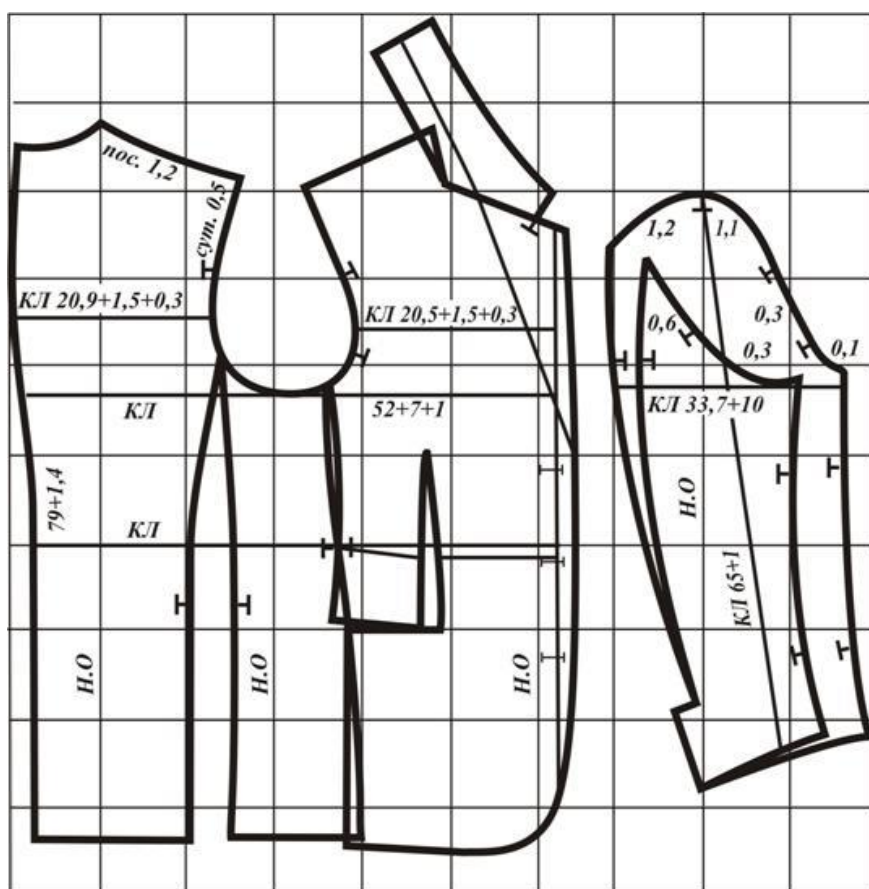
Технический чертеж конструкции мужского пиджака (сетка чертежа 10x10см)
